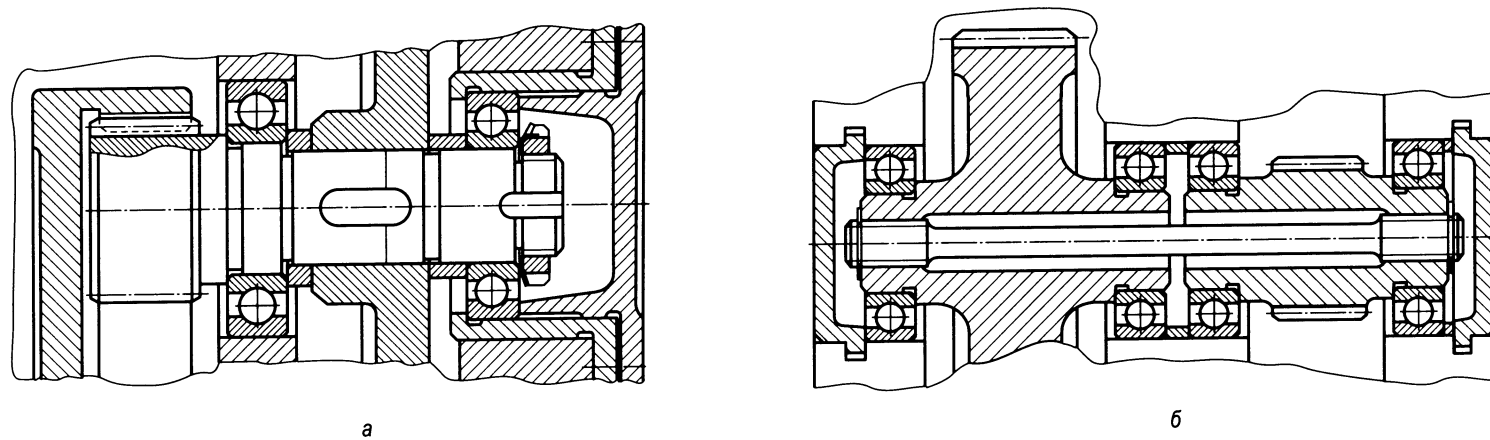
Промежуточный вал цилиндрического редуктора внутреннего зацепления (а) и двухпоточного цилиндрического редуктора (б)
